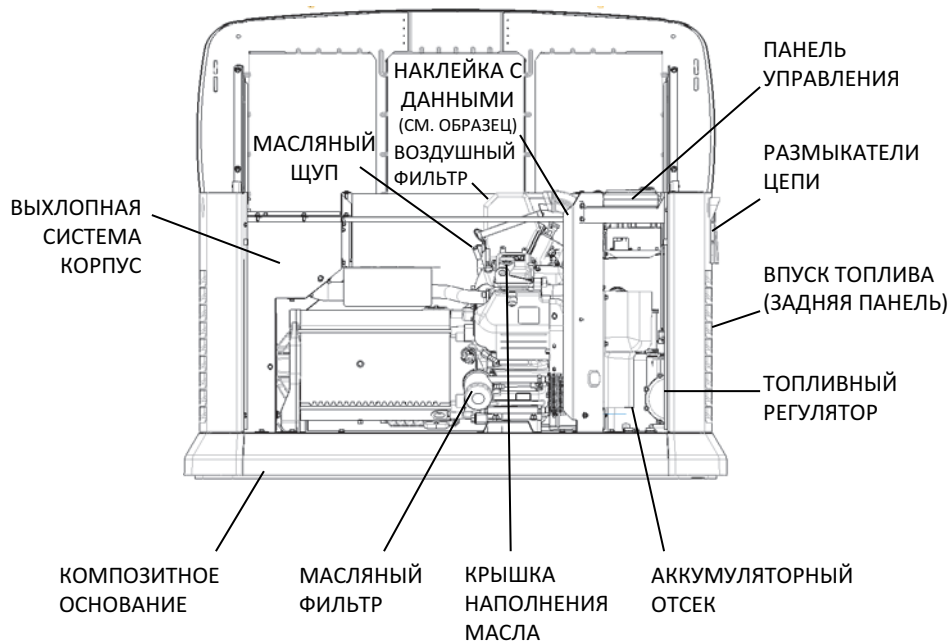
Двигатель GT-990, блок 10 и 13 кВА
